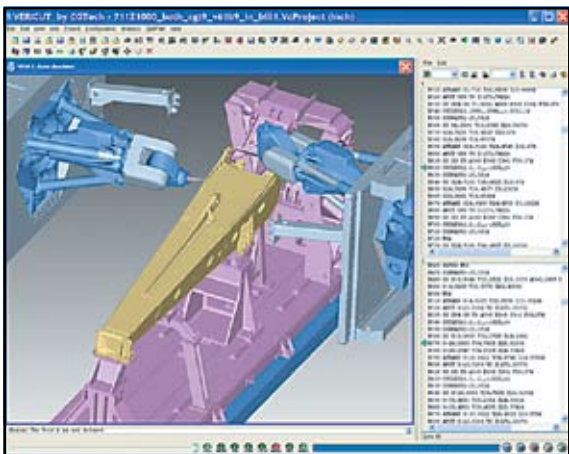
Модель фрезерного обрабатывающего центра с головами типа Tricert
